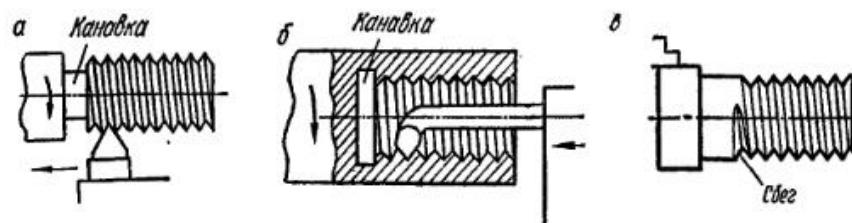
Канавки для выхода резца (*а, б*) и сбег резьбы (*в*)
